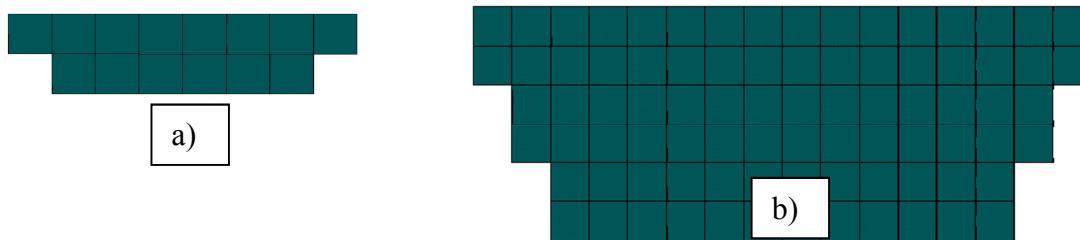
Coupe transversale du cordon. a) : vitesse de soudage 4.3 mm/s. b) : vitesse de soudage 2.6 mm/s
